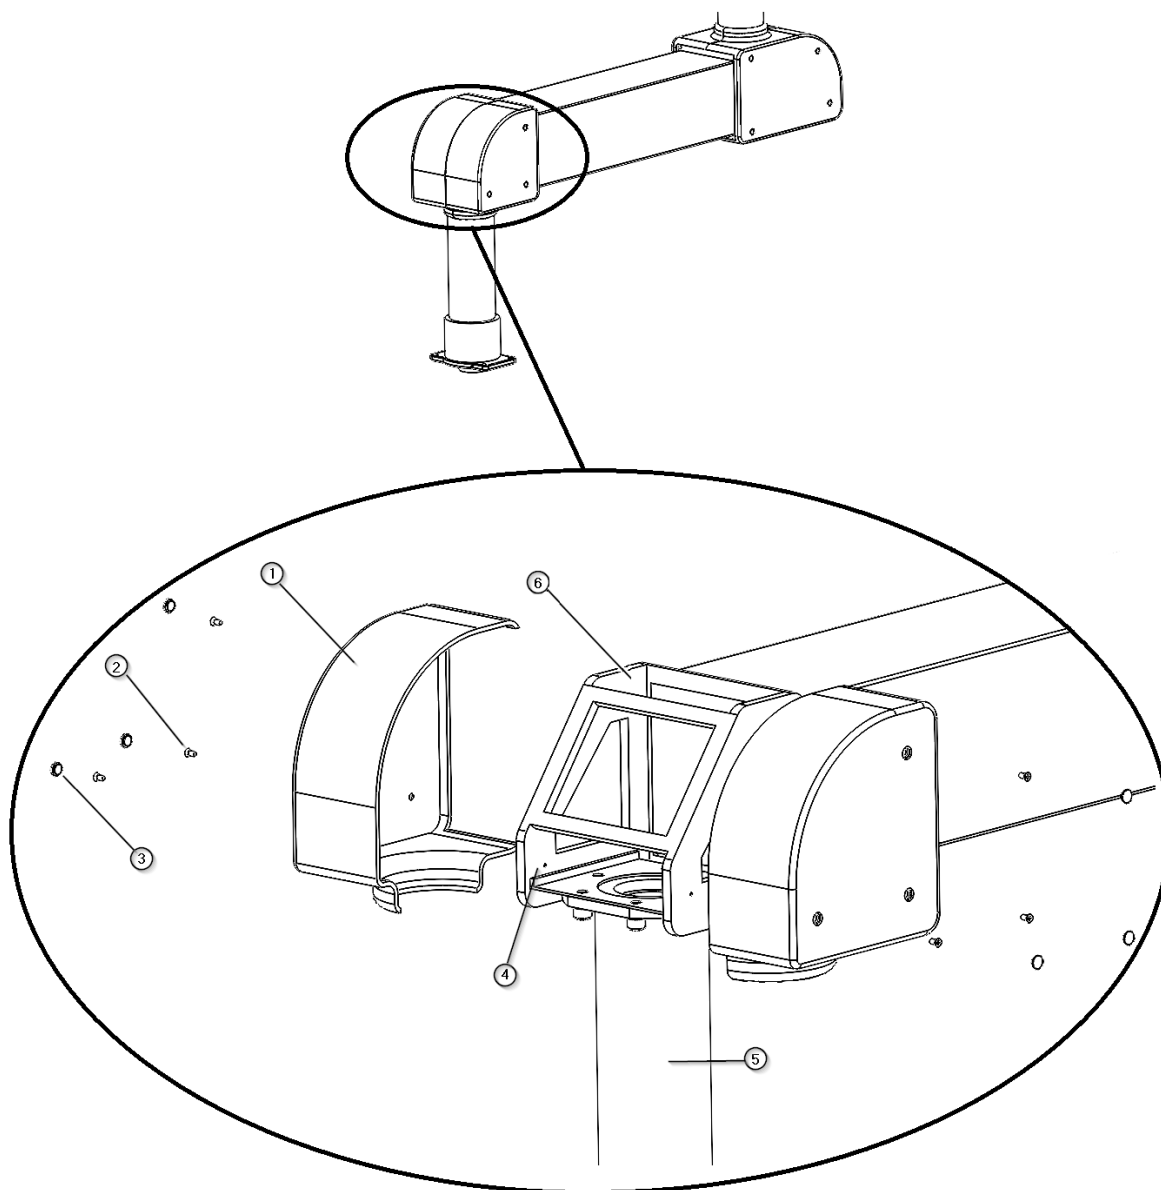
Montaje / desmontaje de tapas protectoras en el tubo de caída de un brazo motor
